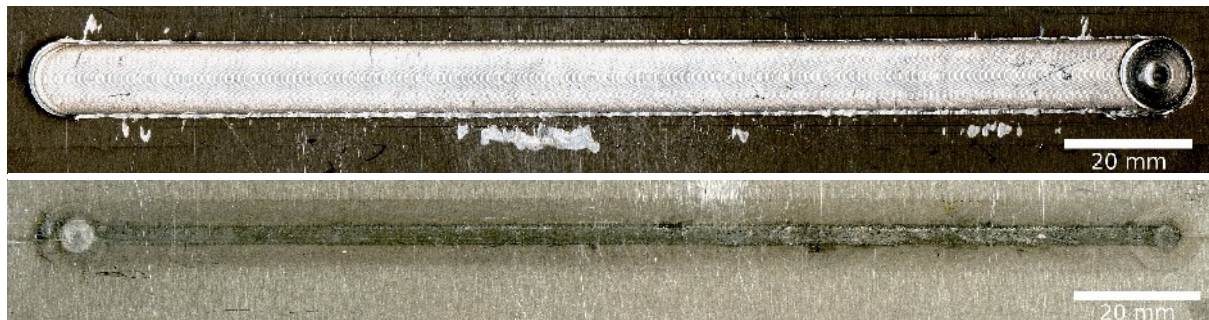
Vzhled svarového spoje (vrchní a spodní část svaru) zhotoveného metodou Friction Stir Welding, AZ31 (1,6 mm, svar kolmo na podélný směr)
